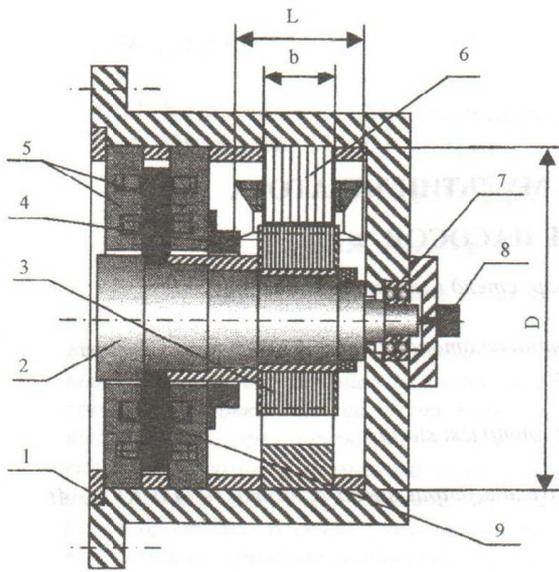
Компоновка радиально-осевого подшипника с двухсторонней разгрузкой: 1 – корпус подшипника; 2 – вал компрессора; 3 – ротор устройства радиальной разгрузки; 4 – датчик радиального положения вала компрессора; 5 – электромагниты осевой разгрузки ротора; 6 – статор устройства электромагнитной разгрузки; 7 – радиально-осевой шарикоподшипник; 8 – датчик осевого положения ротора; 9 – упорный гребень осевой разгрузки
